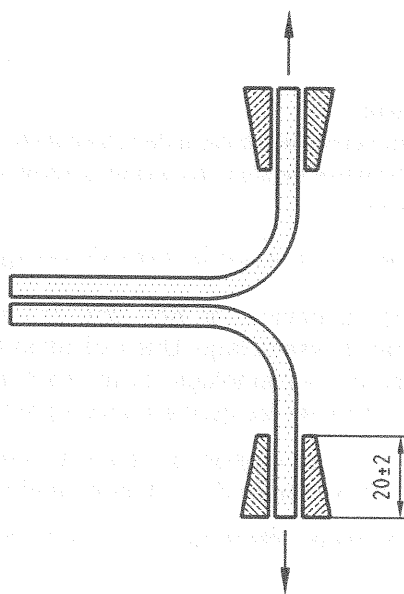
Fixation des éprouvettes pour les essais de pelage
